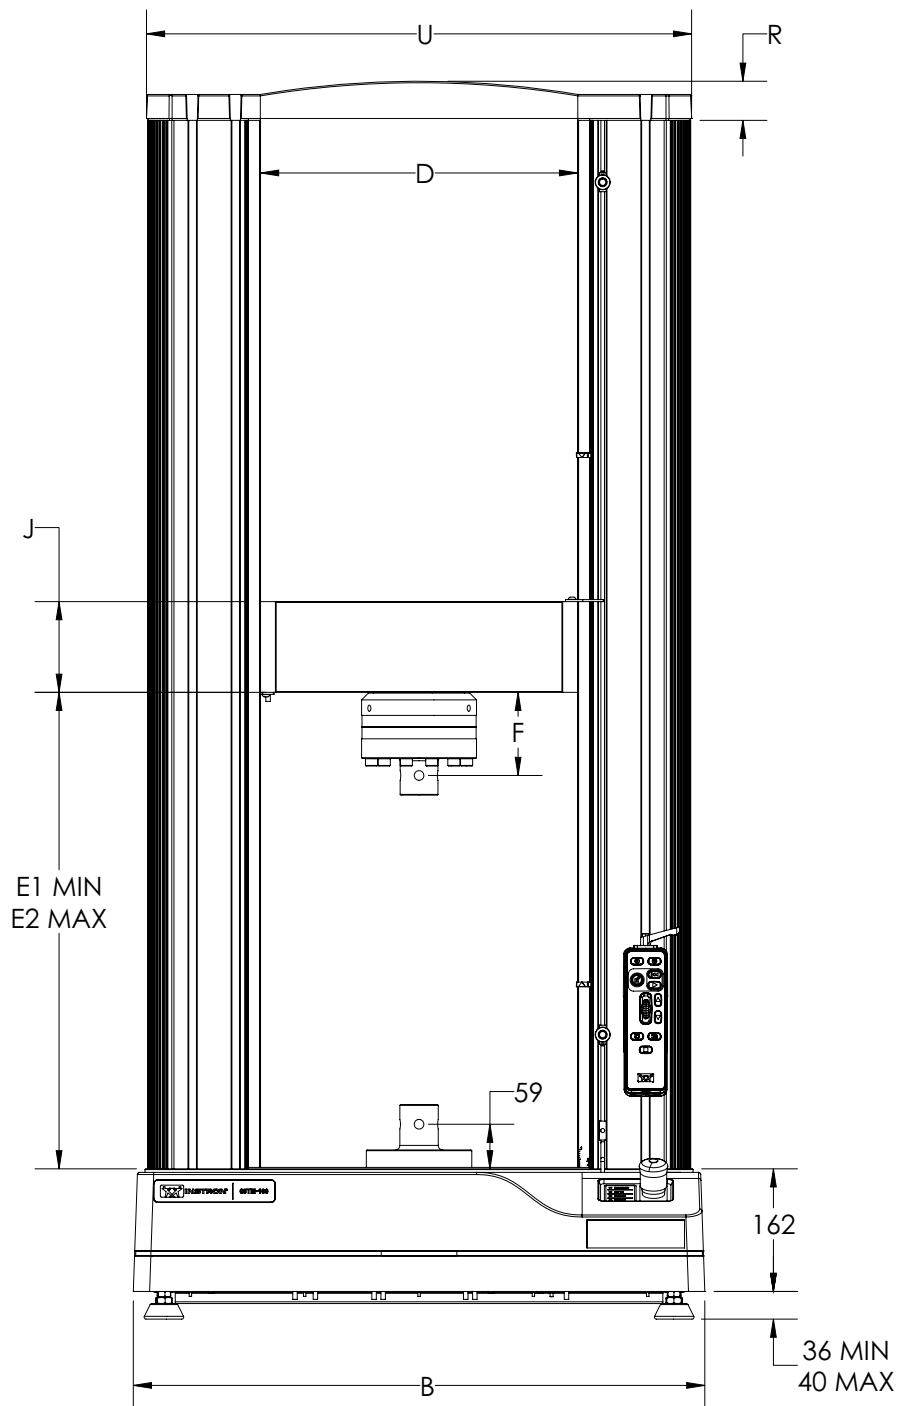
68TM-100 dimensões da estrutura - vista frontal
